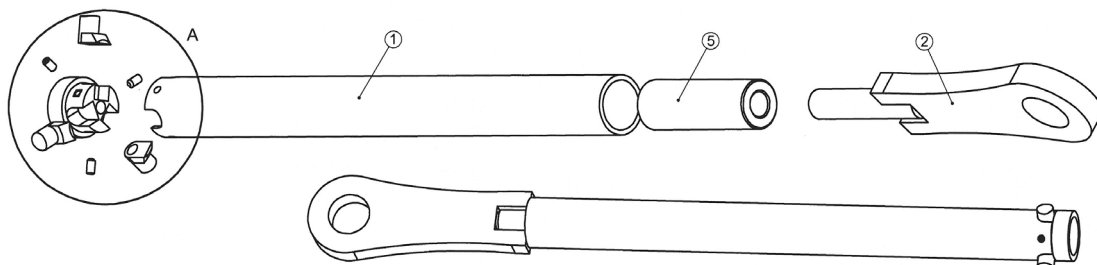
Explosionszeichnung der Bauteile Modul mit linearer Entfaltung
